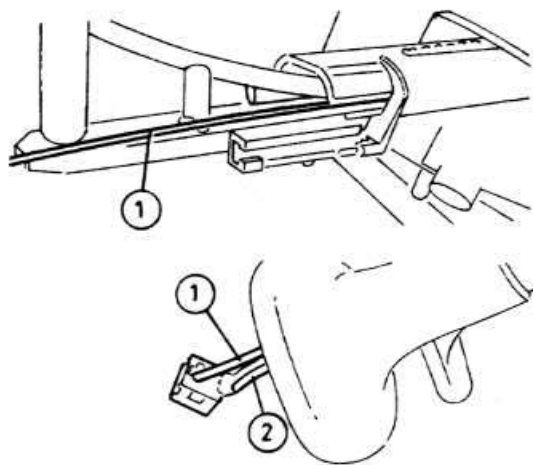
С помощью сварочного электрода (1) вытолкните выключатель от верхней части рычага селектора — отпаяйте подсоединения проводов (2)
